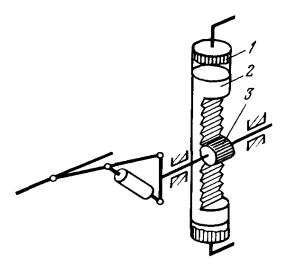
Привод вращения манипулятора: 1 - гидроцилиндр, 2 – плунжер с рейкой, 3 – шестерня.
